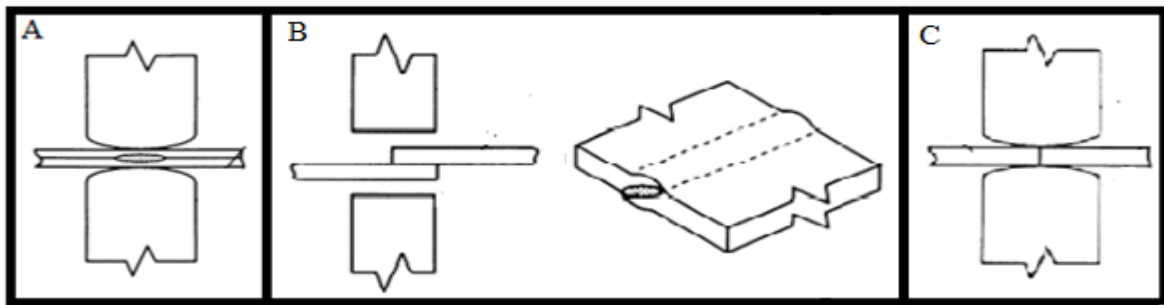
Tipos de juntas utilizadas na soldadura por roletes (RSEW): A-Junta sobreposta, B- Junta topo-a-topo, C-Juntas sobreposta por esmagamento. [17]
